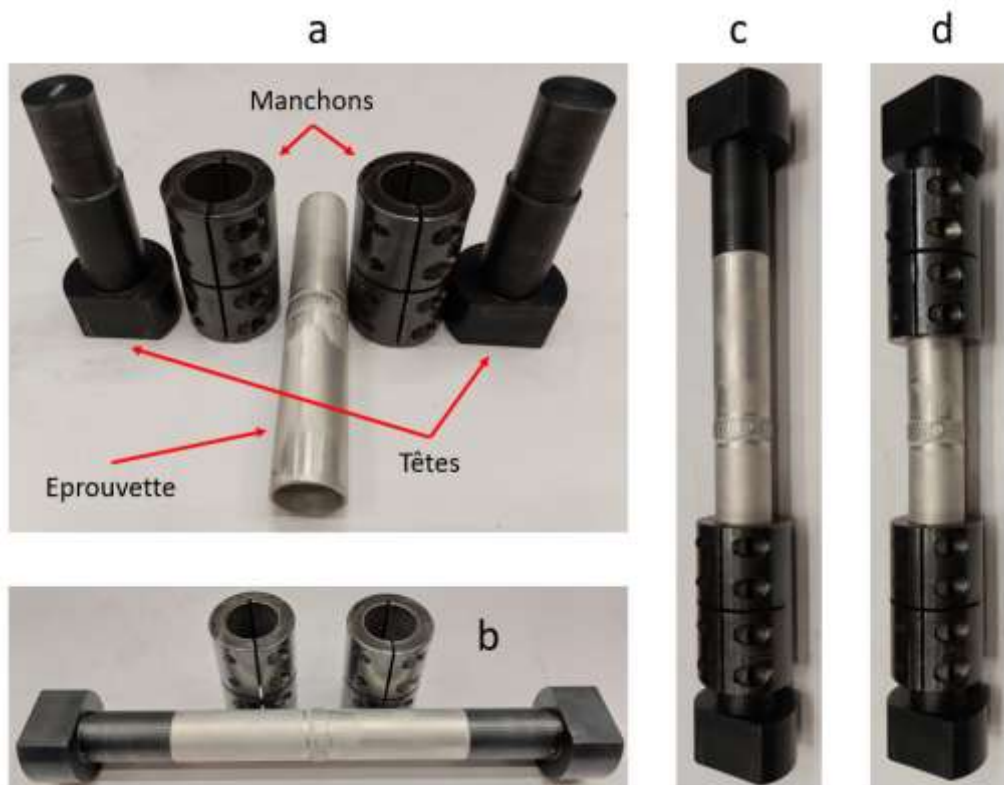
Adaptation des éprouvettes sur les mors. (a) pièces du montage, (b) insertion des têtes dans l'éprouvette, (c) mise en place du premier manchon et (d) assemblage complet
